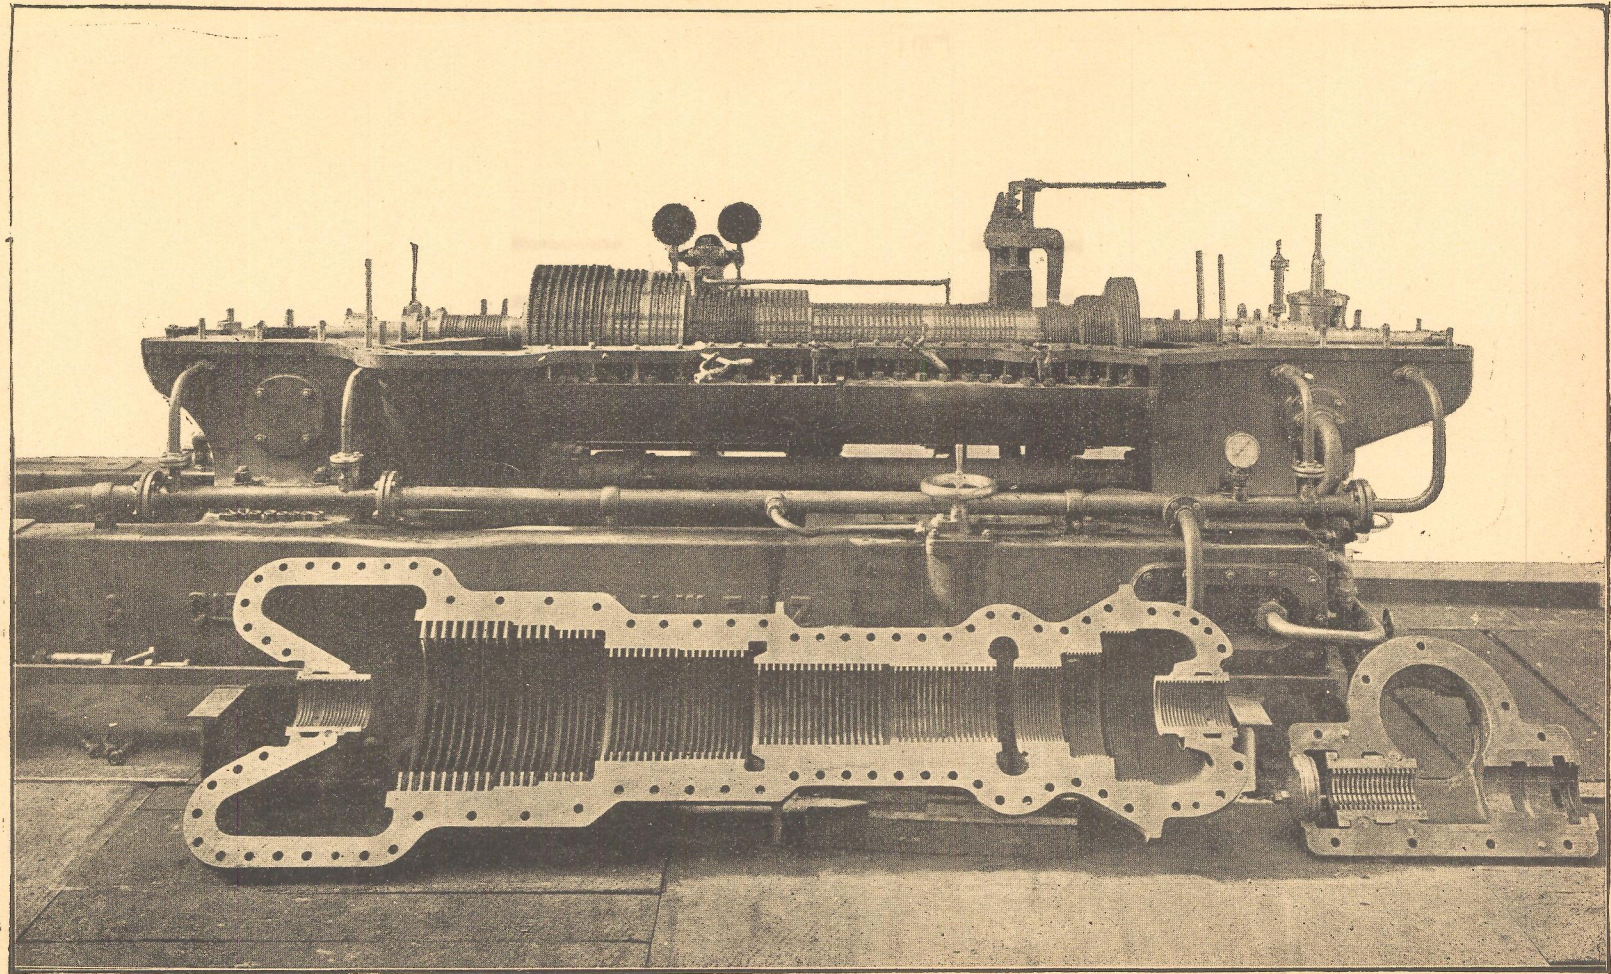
MACHINE DU Puits ZOLLERN II. — *Vue prise de l'arrière.
